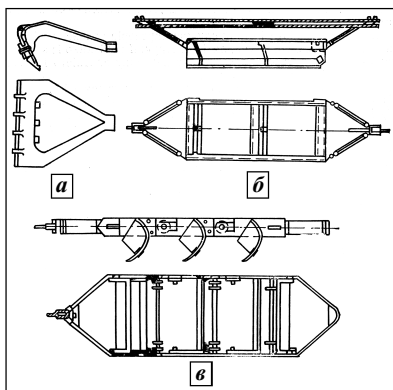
Скрепери: а - гребковий; б - ящиковий; в - багатоковшовий шарнірно-складаний.
